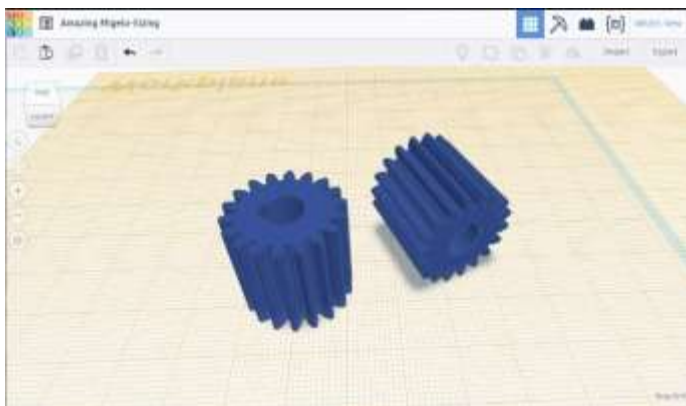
3D - модель зубчастого колеса в TinkerCAD
